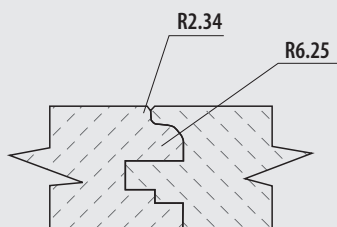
Примеры использования ножевой головки UltraProfiler: выборка дверной четверти, фрезерование контрпрофиля
